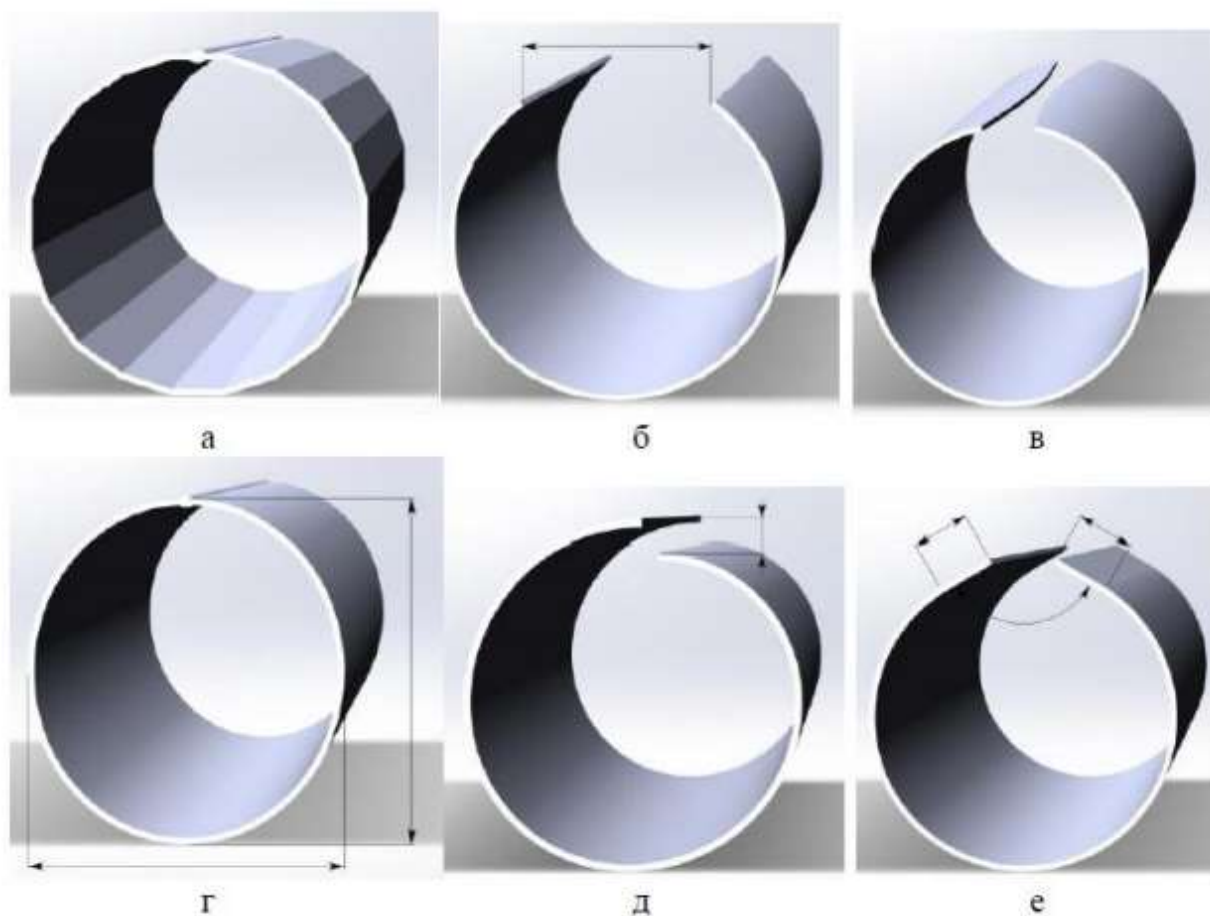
Типовые дефекты труб, трубной заготовки после формовки:
